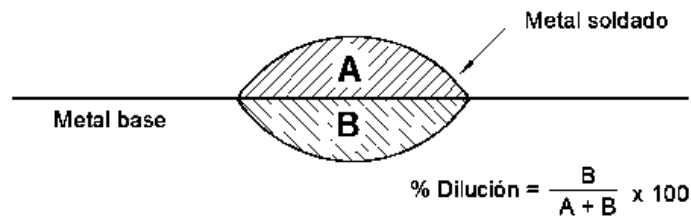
Esquema de Dilución de un Cordón de Soldadura [32]
